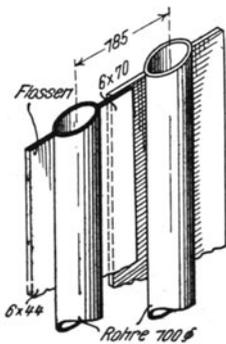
Wasserrohre mit aufgeschweißten sich überlappenden Flossen für Dampfkessel nach Murray.
